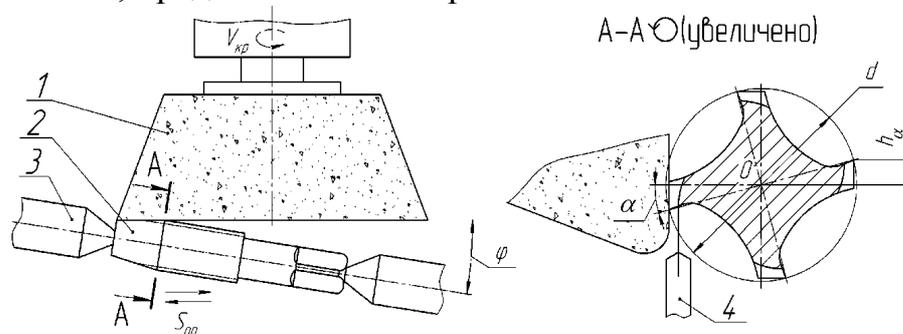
Схема заточки режущей части метчика по задней поверхности
